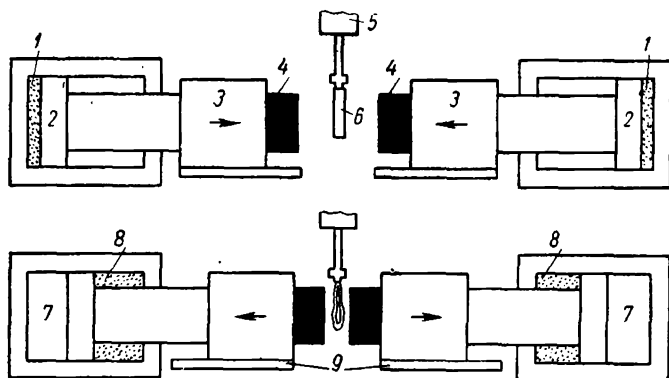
Схема работы импактора. Рабочий ход: 1 — высокое давление сжатого воздуха; 2 — поршень; 3 — бокс; 4 — штамп; 5 — клещи; 6 — заготовка. Обратный (холодный) ход: 7 — клапан открыт для выпуска воздуха; 8 — низкое давление воздуха для возвращения поршня в исходное положение; 9 — направляющие
